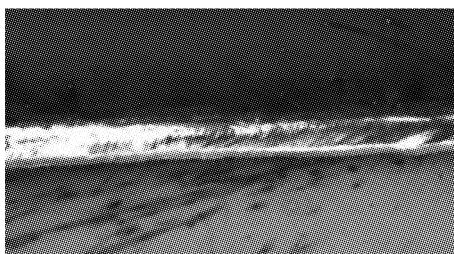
使用 99.99% 高纯氩气焊接的焊缝
